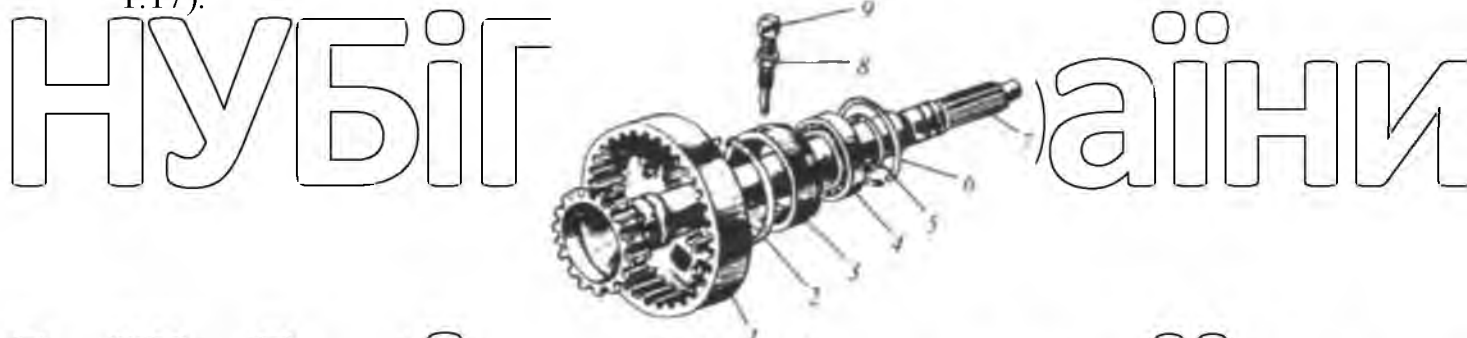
Коронна шестерня в розібраному вигляді: 1 - коронна шестерня; 2 - стопорне кільце 2В110; 3 - стакан/підшипника; 4 - шарикопідшипник 210А; 5 - стопорне кільце 2В50; 6 - стопорне кільце 2В90; 7 - вал; 8 - гайка М12; 9 - гвинт.
